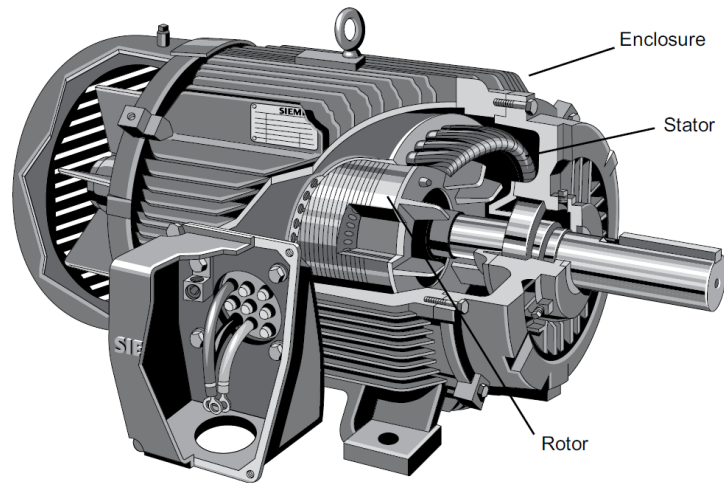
Vue d'ensemble d'une machine asynchrone à simple cage d'écureuil
